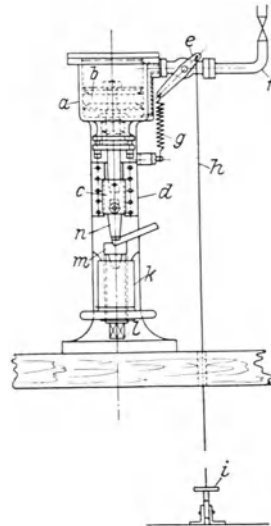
Druckluft-Schweißpresse für das Aufschweißen der Edelstahlplättchen.
